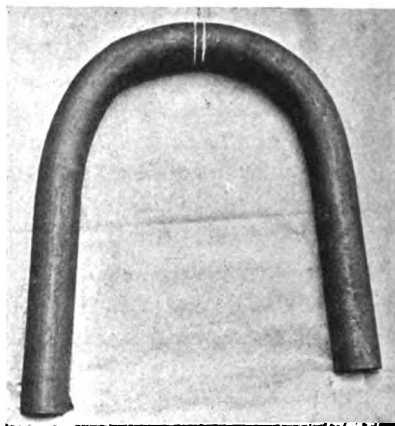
Tube courbé à froid à l'endroit de la soudure.
